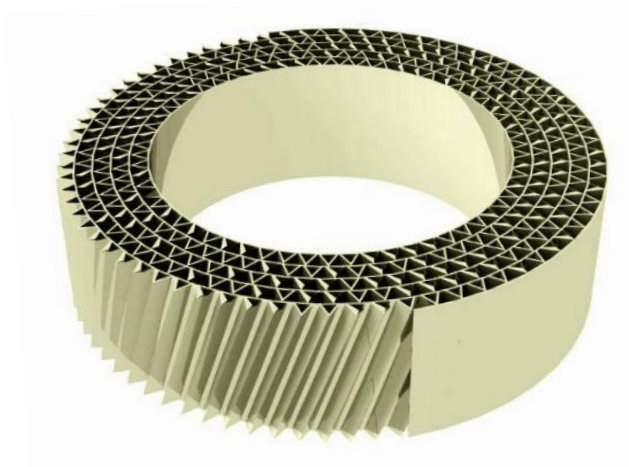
Кольцевой металлический каталитический блок с наклонными спиральными каналами
